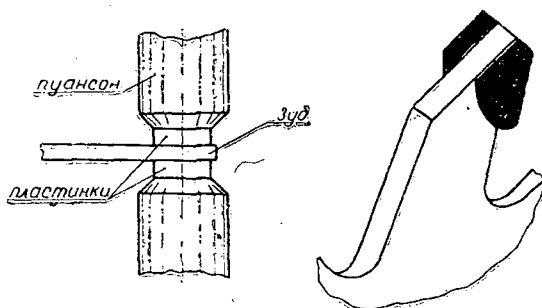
Схема приварки пластинок к боковым граням зубьев пилы.
